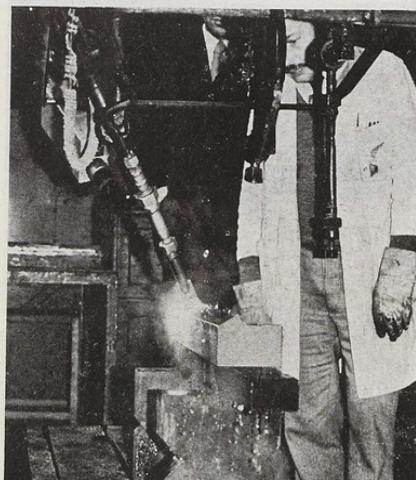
Etude de fontes pour machines-outils : trempe au chalumeau sur éprouvette massive, en forme de glissière (cliché C.T.I.F.-R.N.U.R.).
